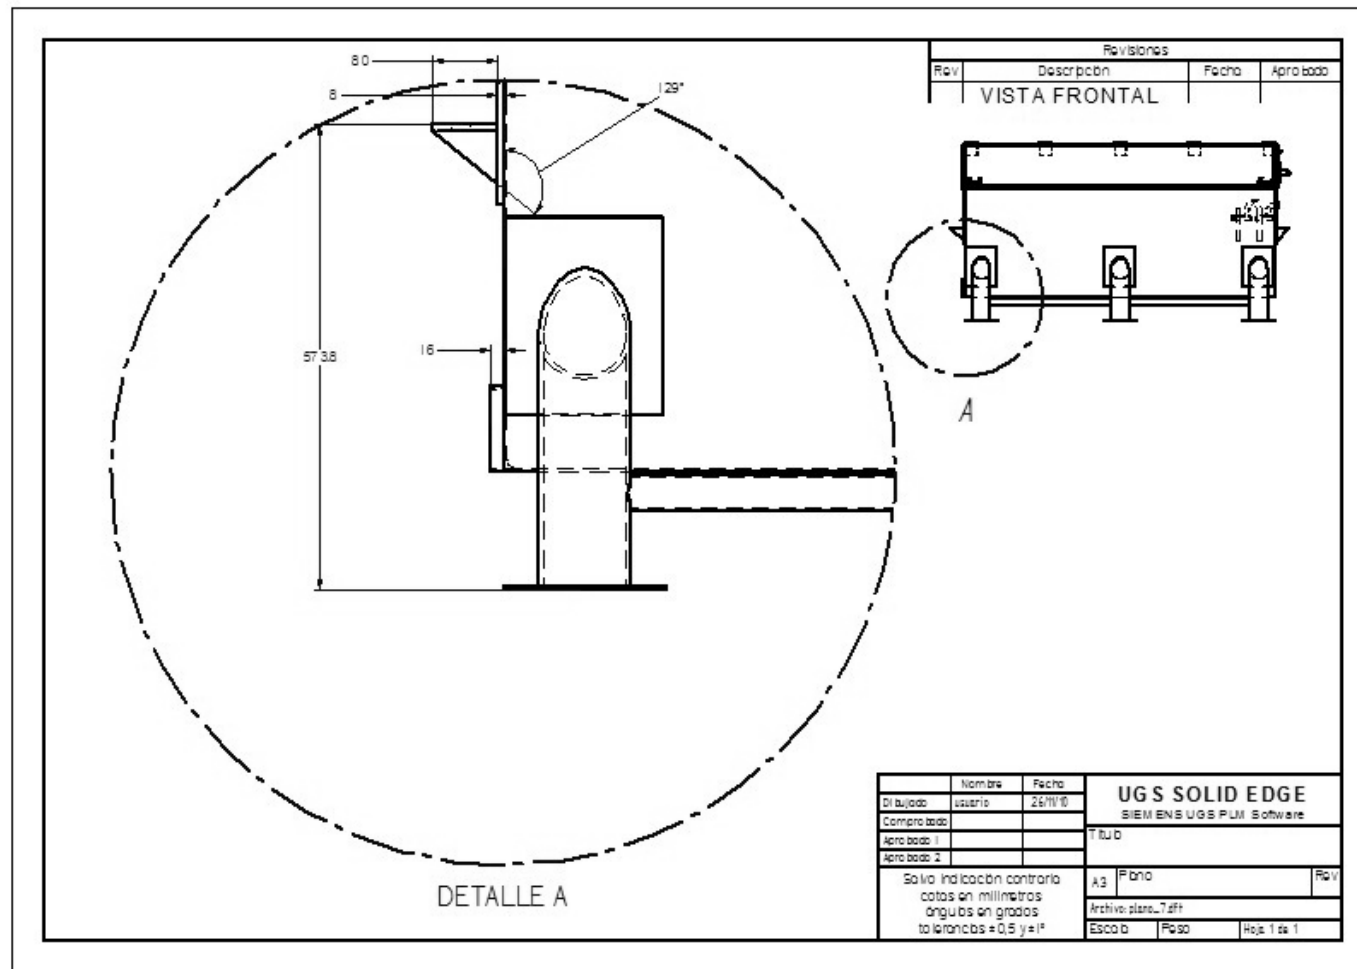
Plano del contenedor de mezclado, vista posterior, detalle 5.
